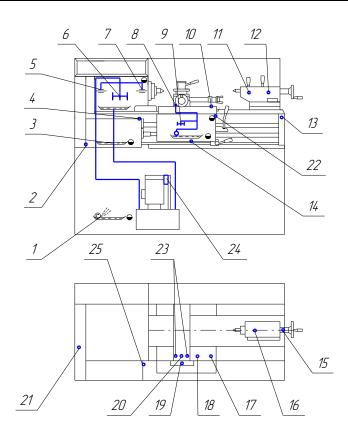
Схема смазки станка Примечание: На некоторых станках реле давления поз. 24 может отсутствовать.
